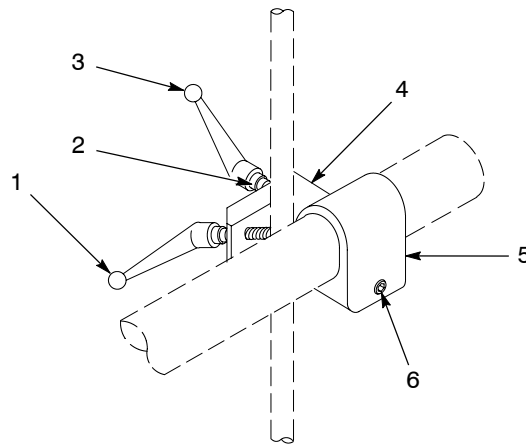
Стандартный штанговый монтажный узел для трубных распылителей
